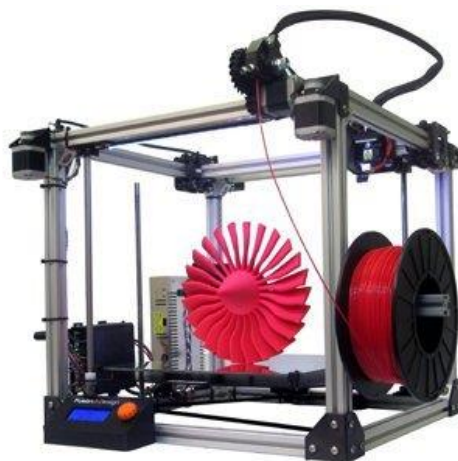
Impressora equipada com Extrusor de Bowden [19]
